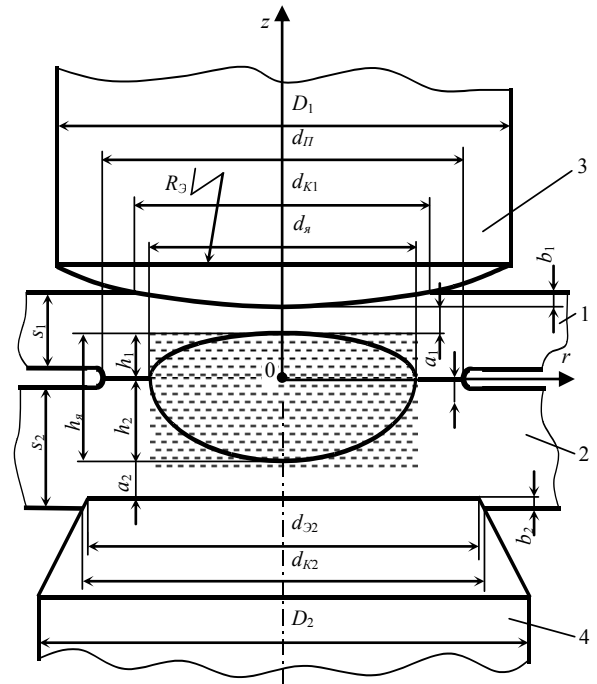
Схема геометрических параметров точечного сварного соединения деталей 1 и 2 разных толщин (при КТС с использованием электродов со сферической 3 или плоской 4 рабочими поверхностями)
